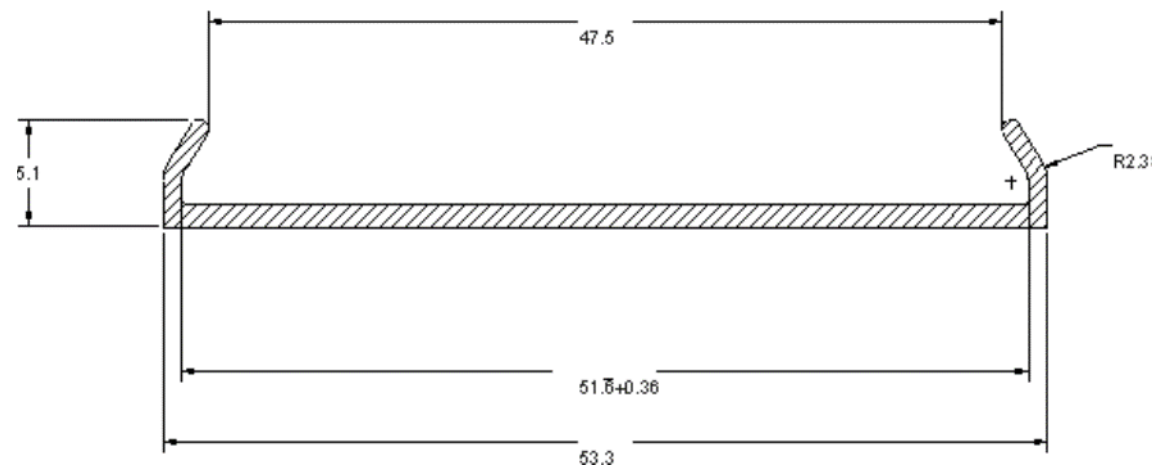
Largura, espessura e detalhes da base metálica em milímetros.
